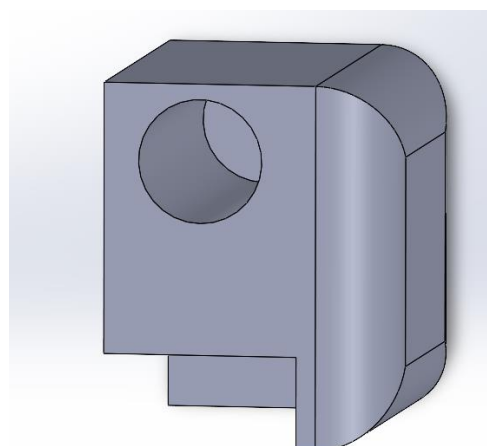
Widok od boku obrazujący element mechanizmu śrubowo-tocznego – nakrętki.
